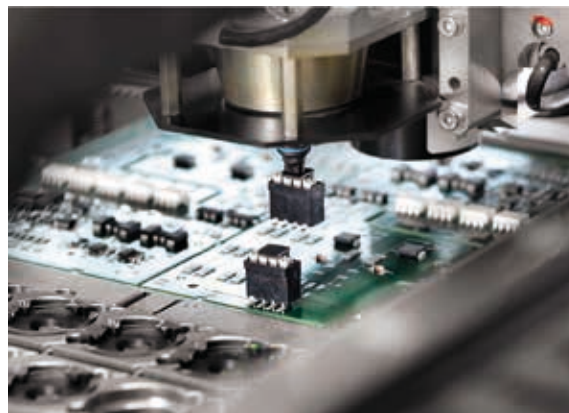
Pick+Place-Prozess für SMT-Leiterplattenverbinder – Quelle: Weidmüller
